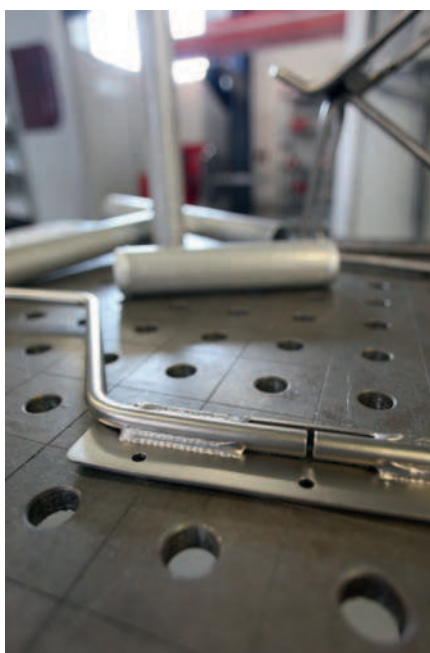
• Mit dem Roboter geschweißter Spezialgepäckträger für ein Lastenfahrrad.
